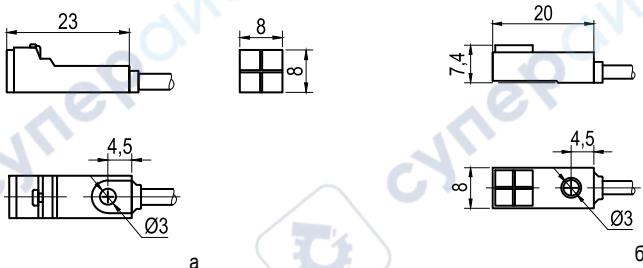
Габаритные и установочные размеры датчиков с шириной корпуса 8 мм
